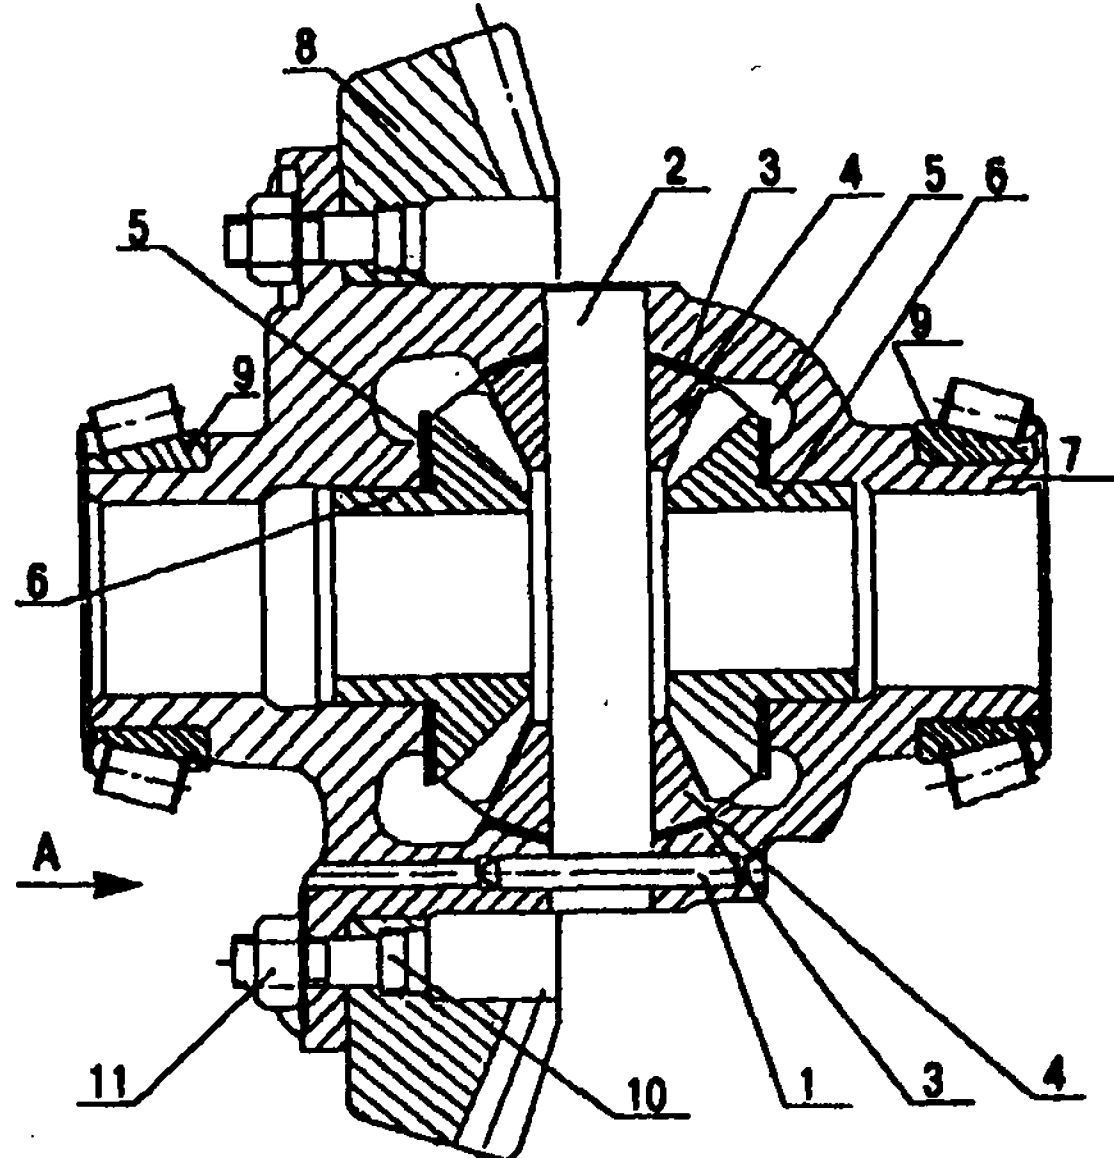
Дифференциал в сборе с ведомой шестерней: 1 - стопор оси сателлитов; 2 - ось сателлитов; 3 - шайба сателлитов; 4 - сателлит; 5 - шайба шестерни; 6 - полуосевая шестерня; 7 - корпус дифференциала; 8 - ведомая шестерня; 9 - внутреннее кольцо с роликами подшипника дифференциала; 10 - болт; 11 - гайка
